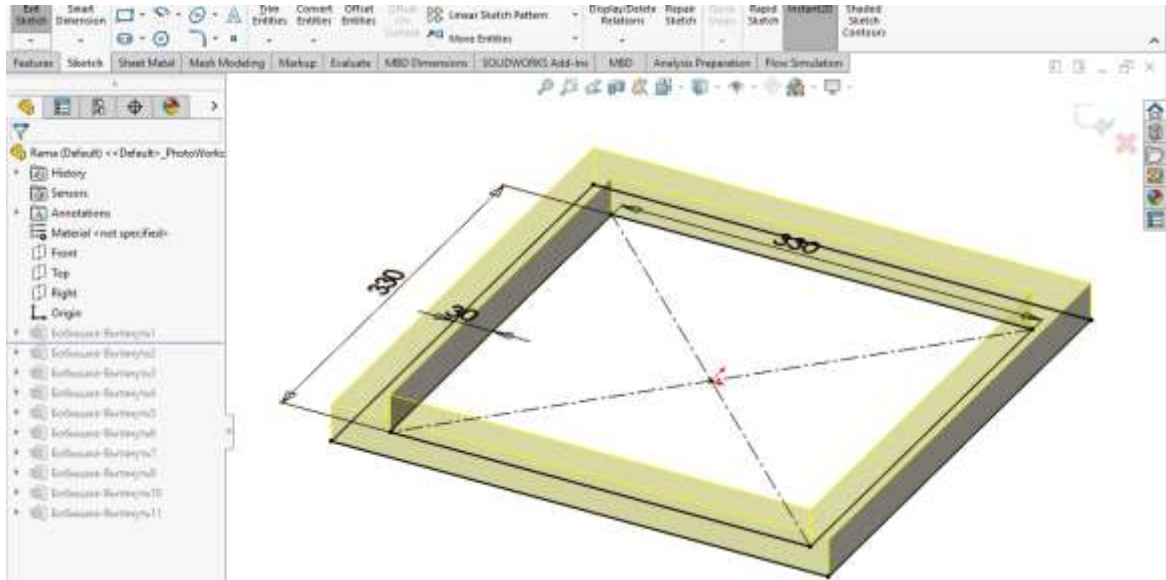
Модель верхньої рамки основного тіла установки
